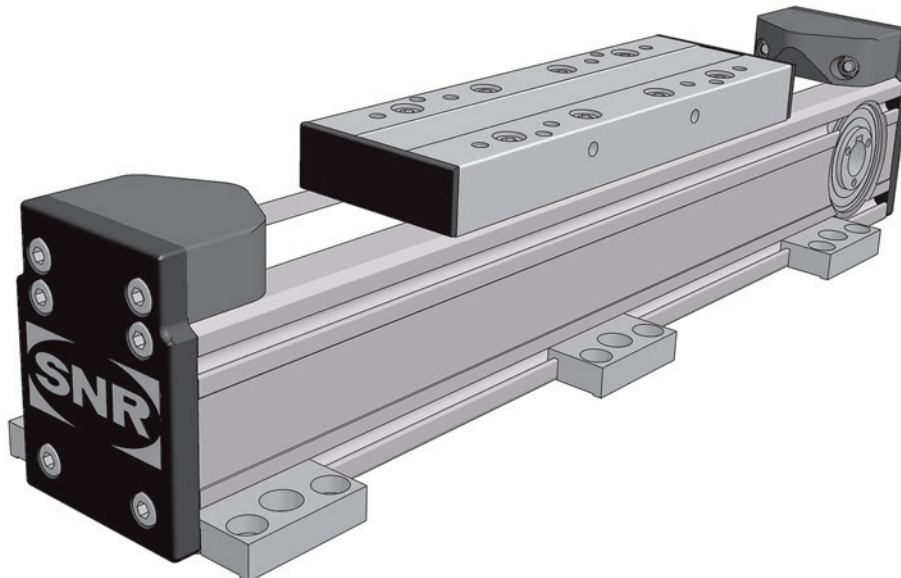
Linearachse AXC mit Befestigungsleisten
